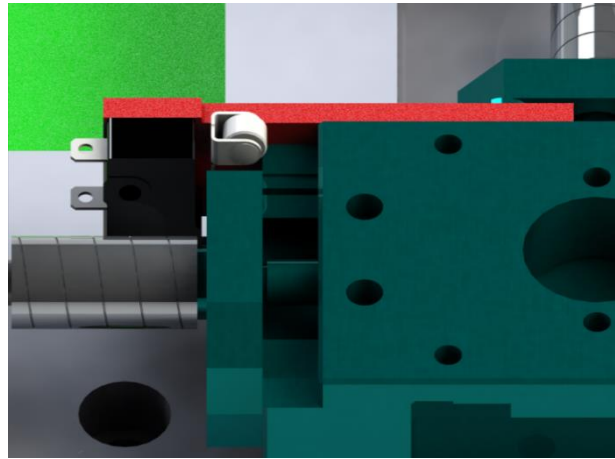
Mínima invasión del micro switch de Motor X montado al posicionador
